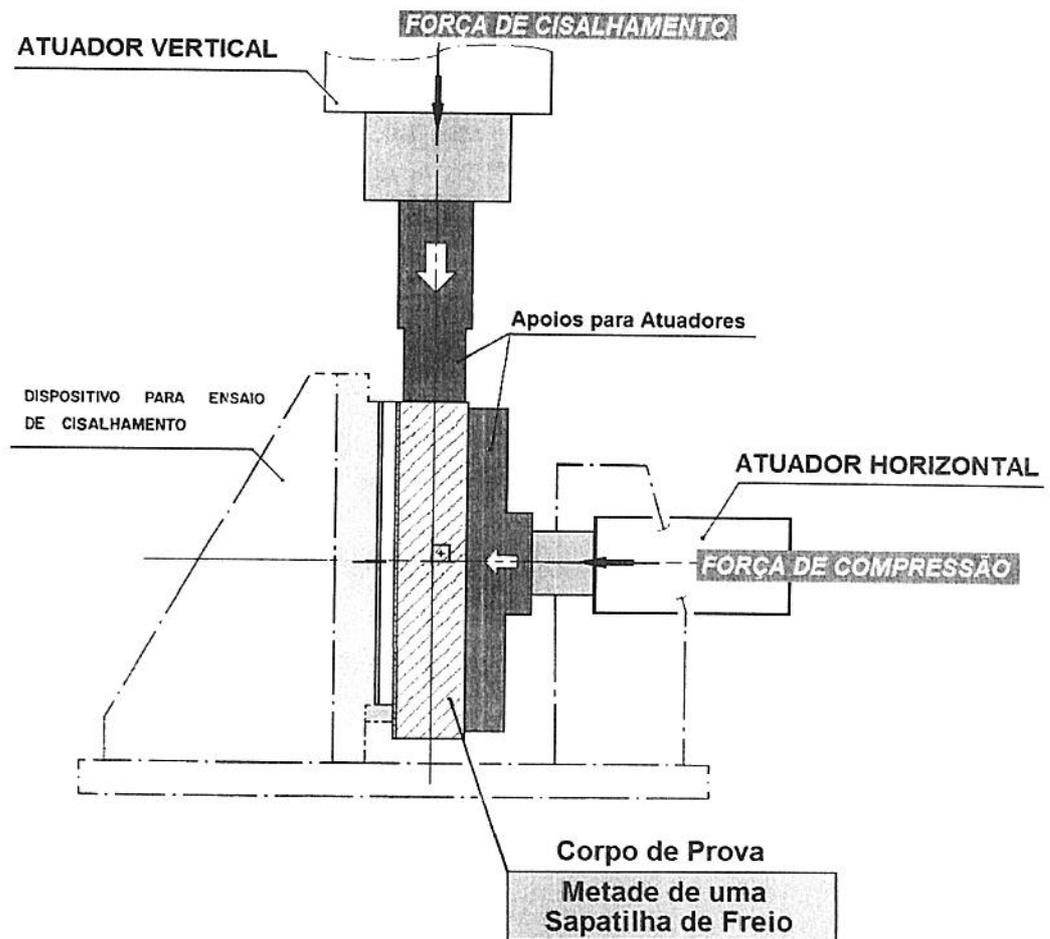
Ensaio de Cisalhamento da Aderência – Arranjo típico (Vista Lateral)
